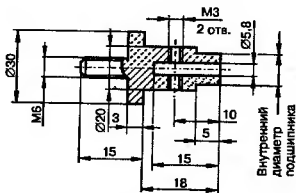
Чертеж насадки для крепления лопастей ветряного колеса
